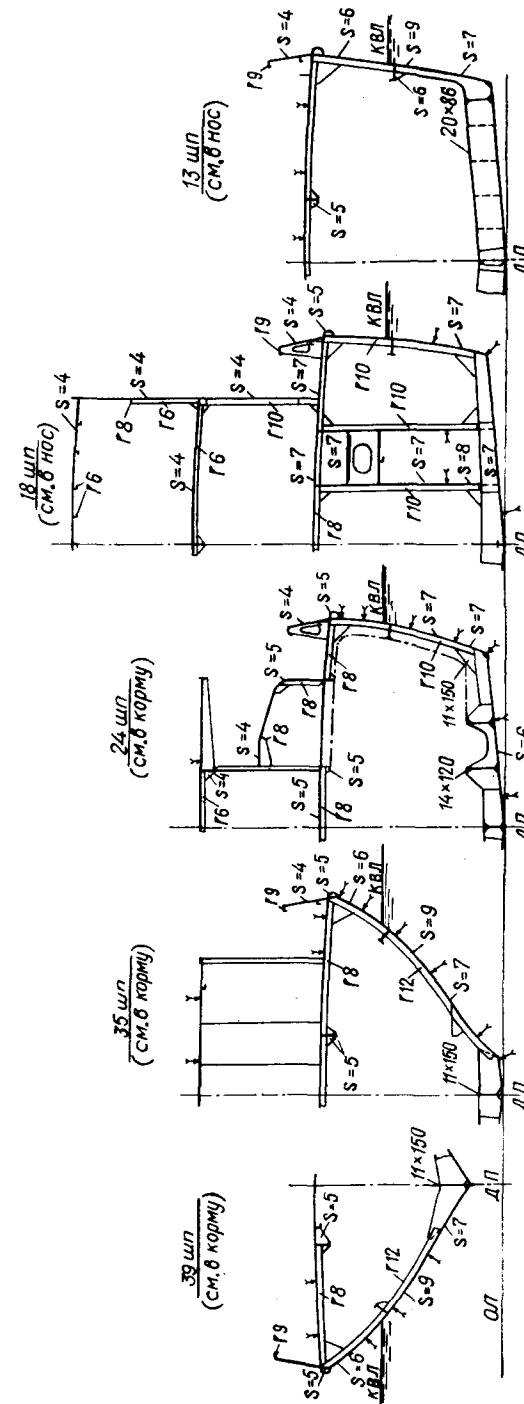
Конструктивные сечения корпуса буксира *Марс*.
